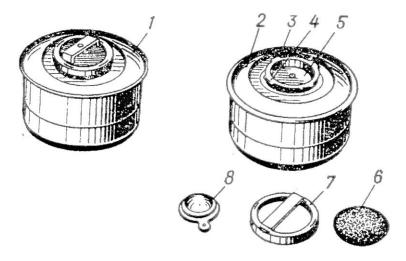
Фильтрующе-поглощающая коробка EO.1.15.01: 1 — фильтрующе-поглощающая коробка EO.1.15.01 в сборе; 2 — корпус; 3 — горловина; 4 — фланец; 5 — клапан вдоха; 6 и 8 — пробки; 7 — обтекатель
